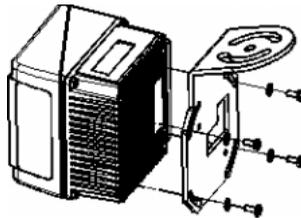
Befestigung des ST-237 Montagewinkels
